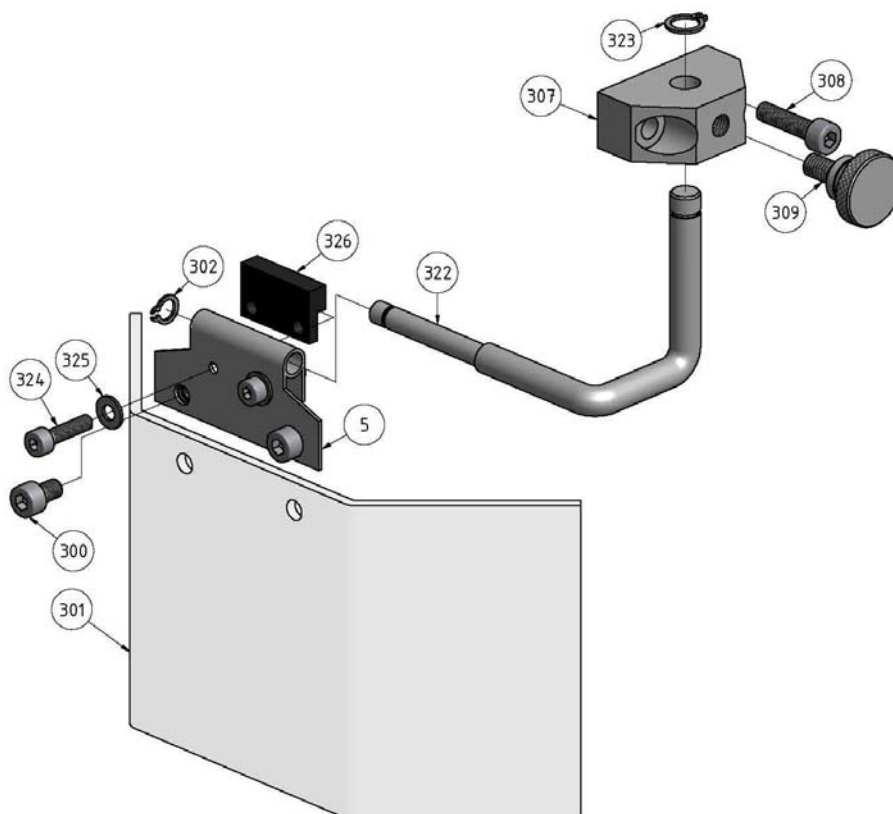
Fräsfutterschutz - Milling chuck protection
